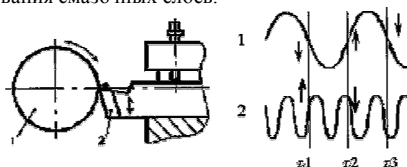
Схема колебательных движений заготовки 1 и режущего инструмента 2 в процессе резания.
